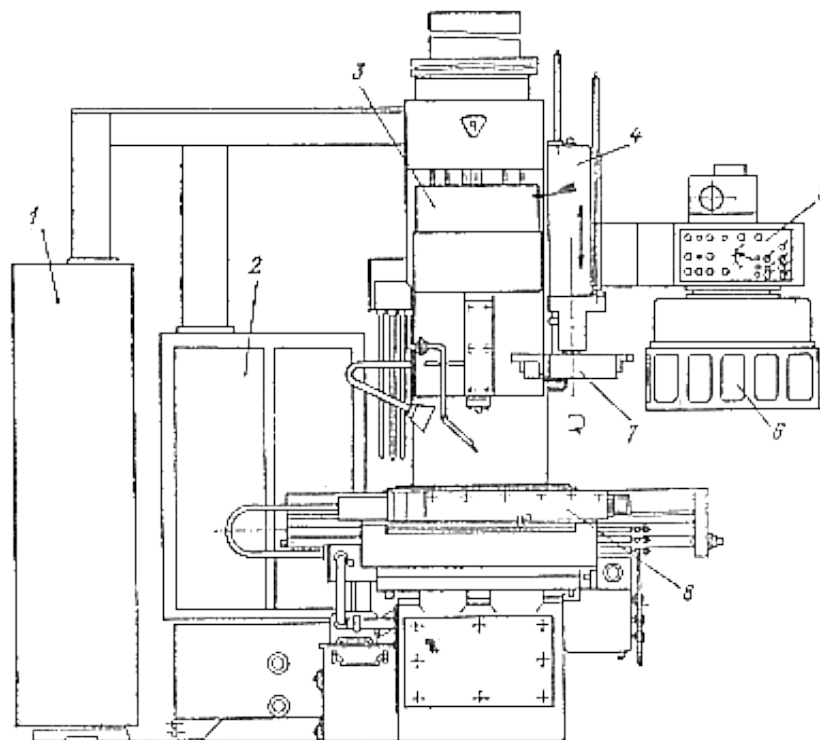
Багатоопераційний вертикально-фрезерний верстат моделі ЛФ260-МФ4 з автоматичною зміною інструменту: 1 - шафа системи ЧПК; 2 - електрошафа верстата; 3 - повзун шпинделя; 4 - повзун в привід автооператора; 5 - пульт управління верстата; 6 - барабан магазину інструментів; 7 - автооператор; 8 - стіл
